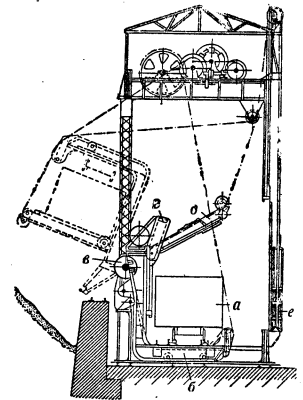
Боковой опрокидыватель: а—вагон; б—люлька, поворачиваемая вокруг оси е; г—совок; д—балки, автоматически удерживающие вагон и находящиеся под действием противовесов е.
